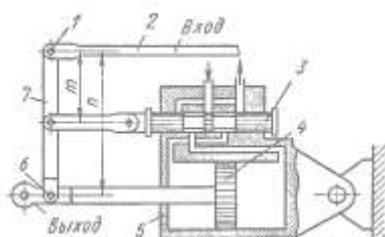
Схем гидроусилителя золотникового типа с обратной связью: 1 - шарнир; 2 - тяга; 3 - золотник распределителя; 4 - поршень; 5 - корпус силового цилиндра; 6 - шарнир; 7 - дифференциальный рычаг
